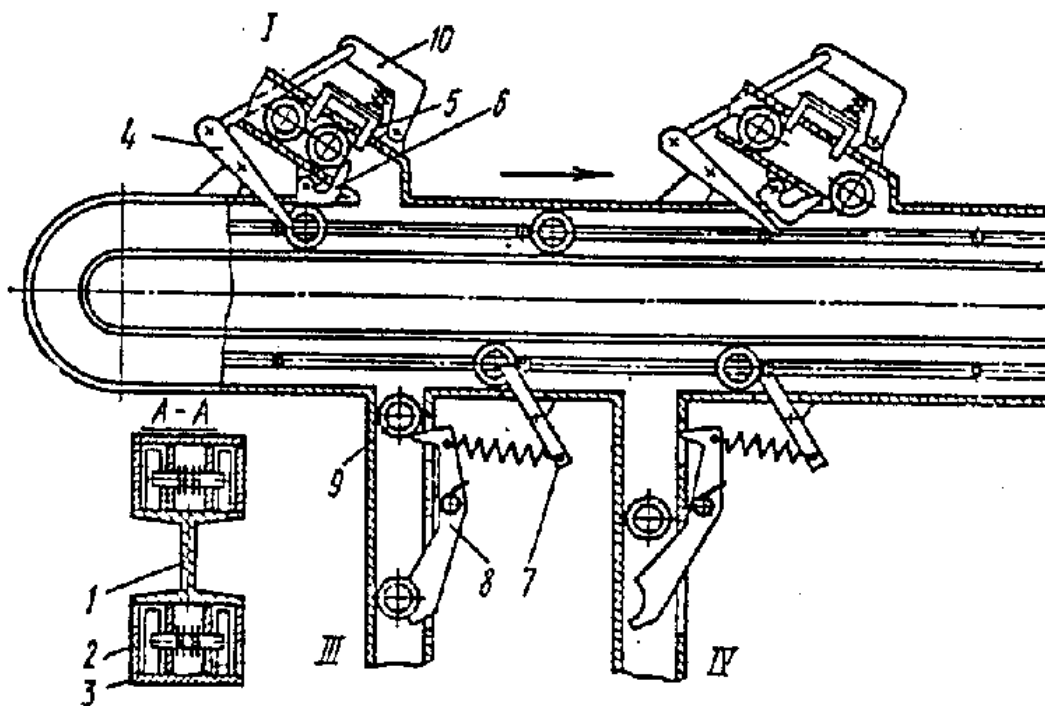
Транспортер-распределитель цепного типа с принудительным перемещением изделий
